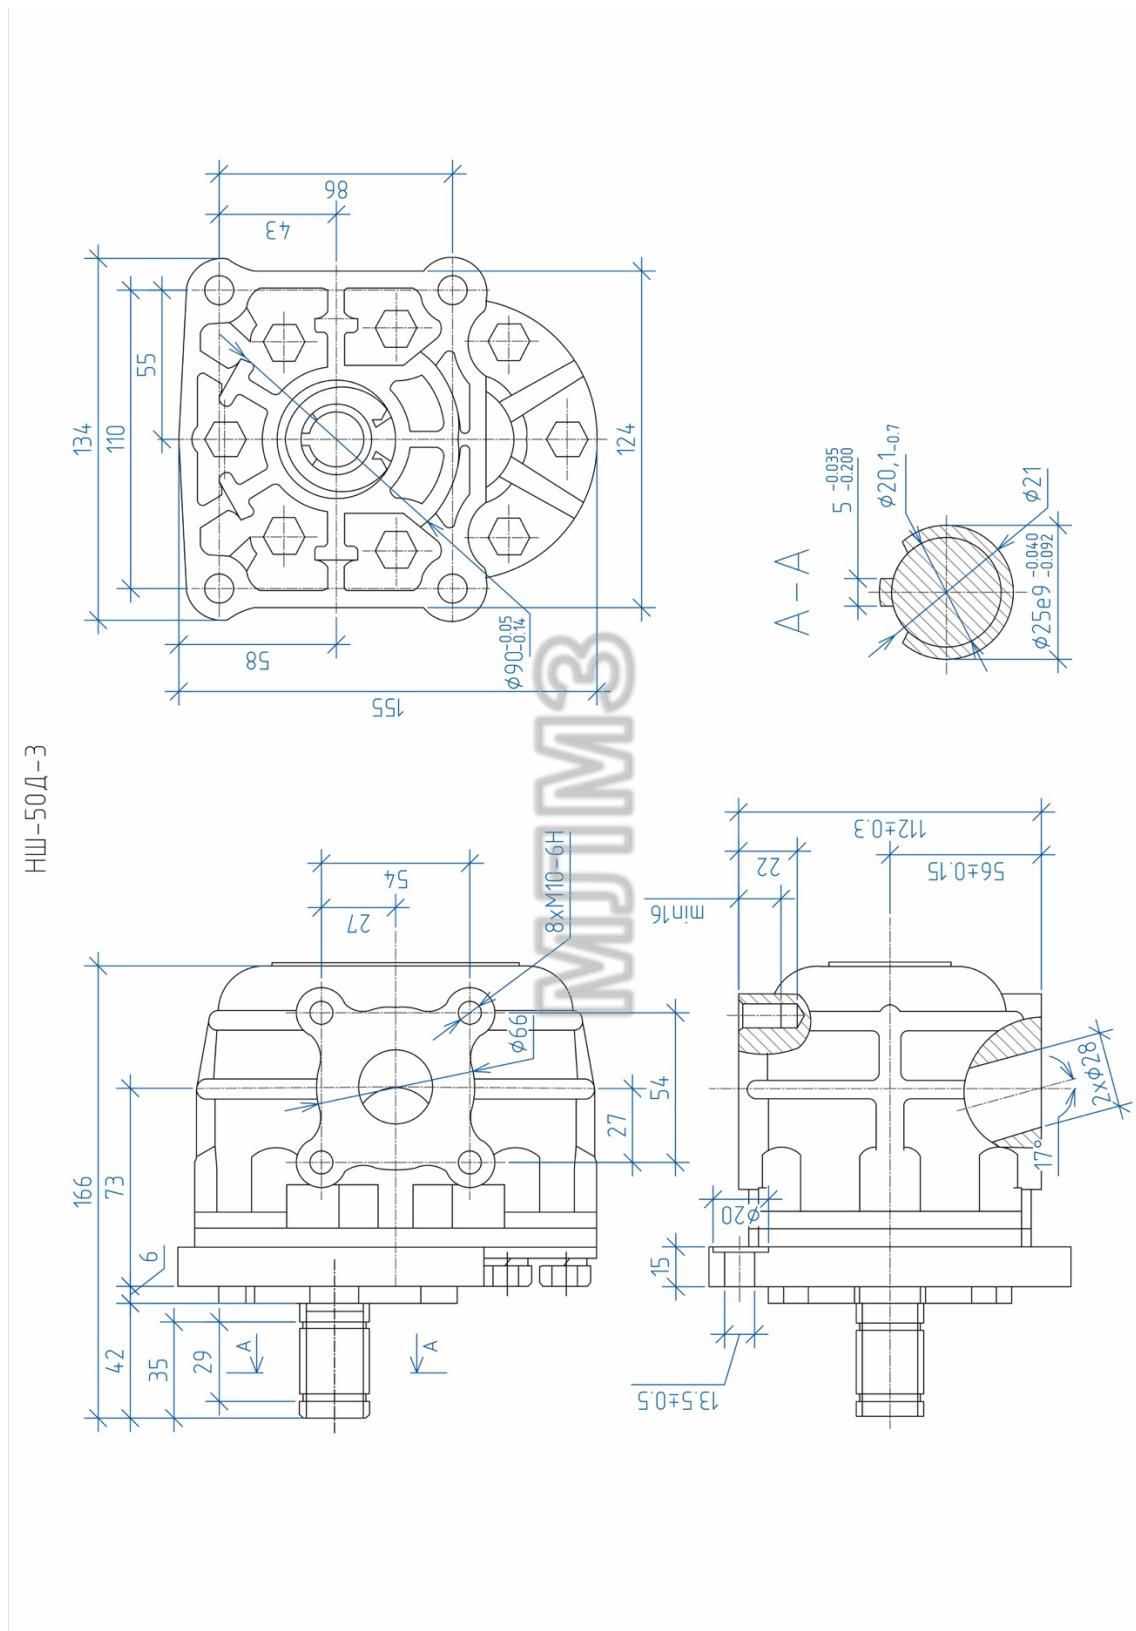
Насосы шестеренные НШ50Д-3, НШ50Д-3Л. Габаритные и присоединительные размеры.
